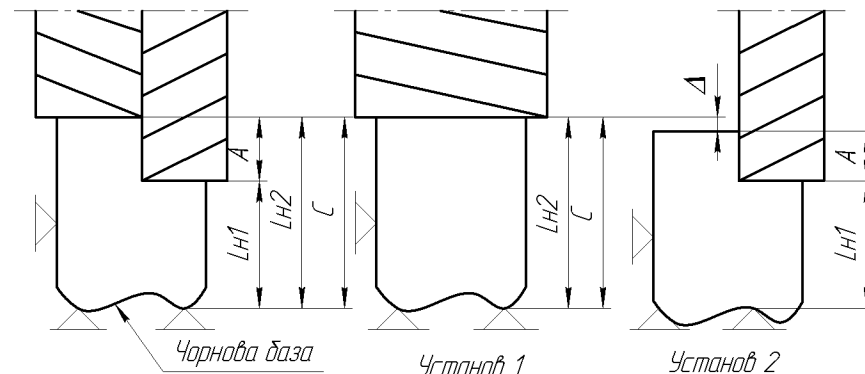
Обробка з одного установа (варіант 1), повторна установка на чорнову базу (варіант 2)
